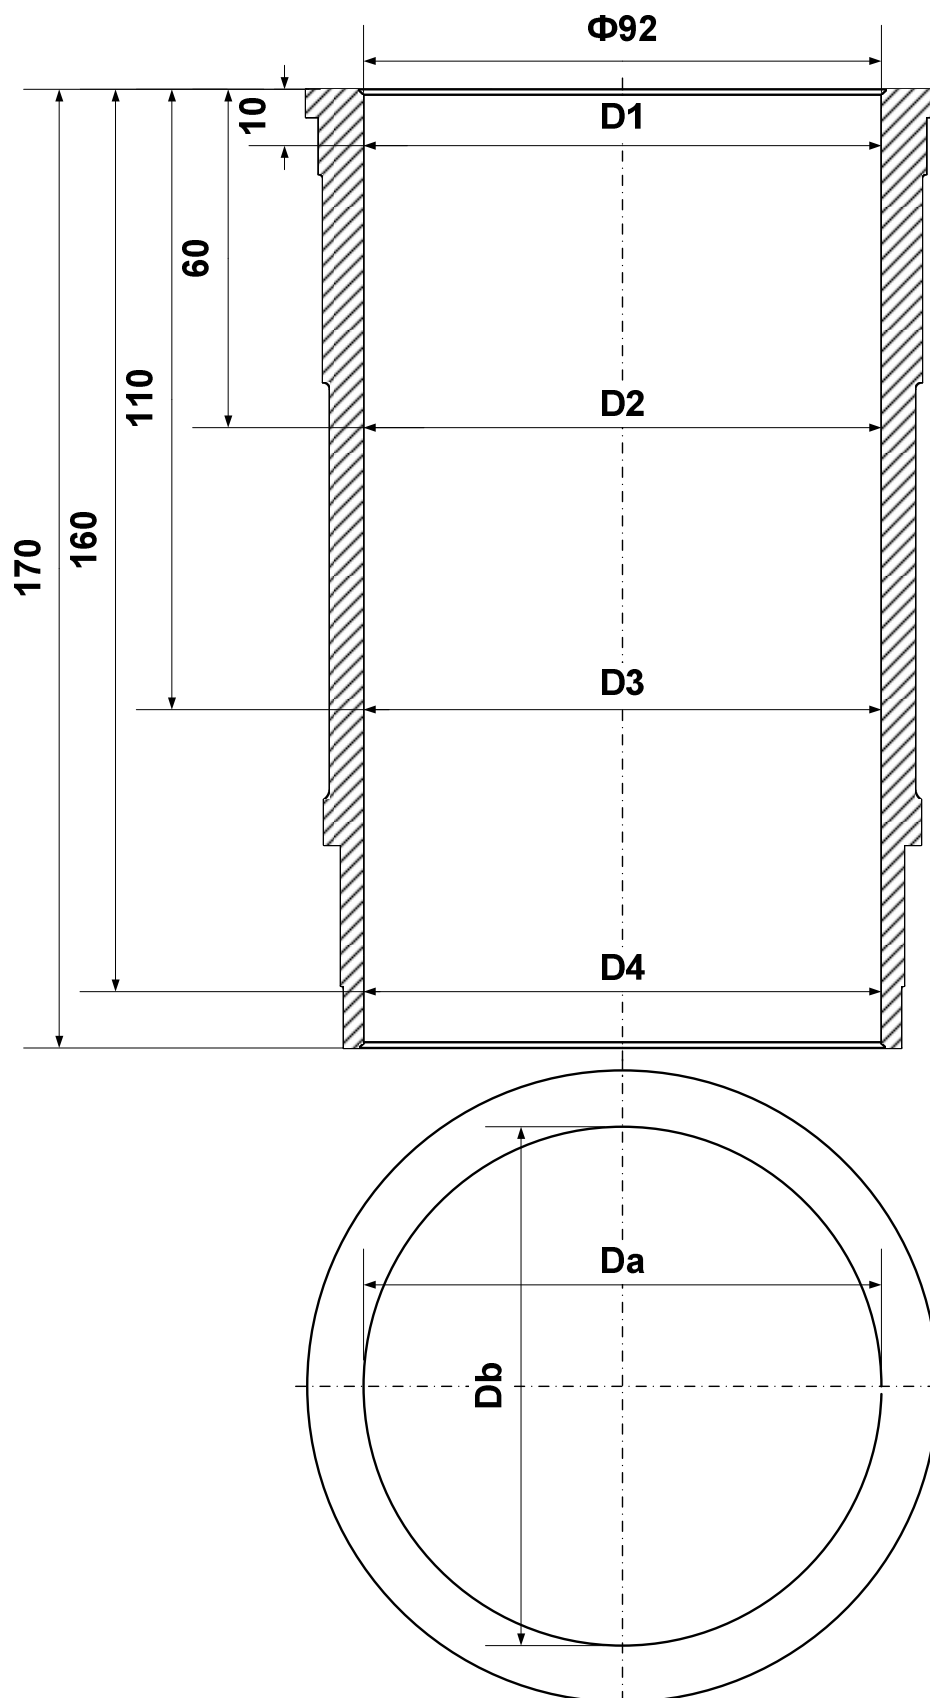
Схема измерений рабочей поверхности гильзы цилиндра
